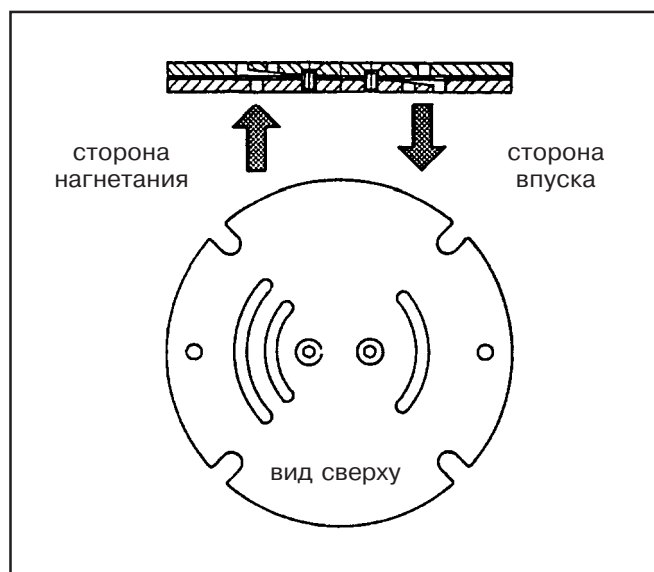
Головка цилиндра первой ступени блоков Manirer и K14
